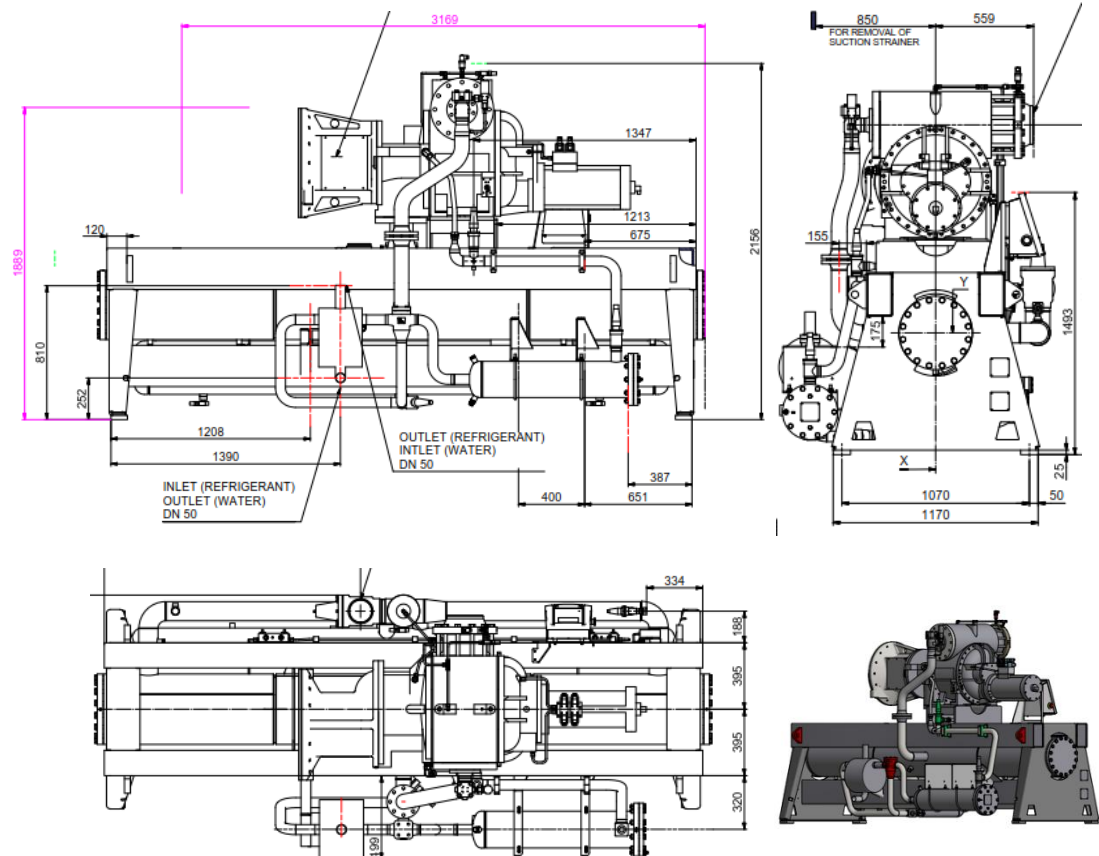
Kältemaschine mit Schraubenverdichter „Johnsons Controls“ – Technische Zeichnung
